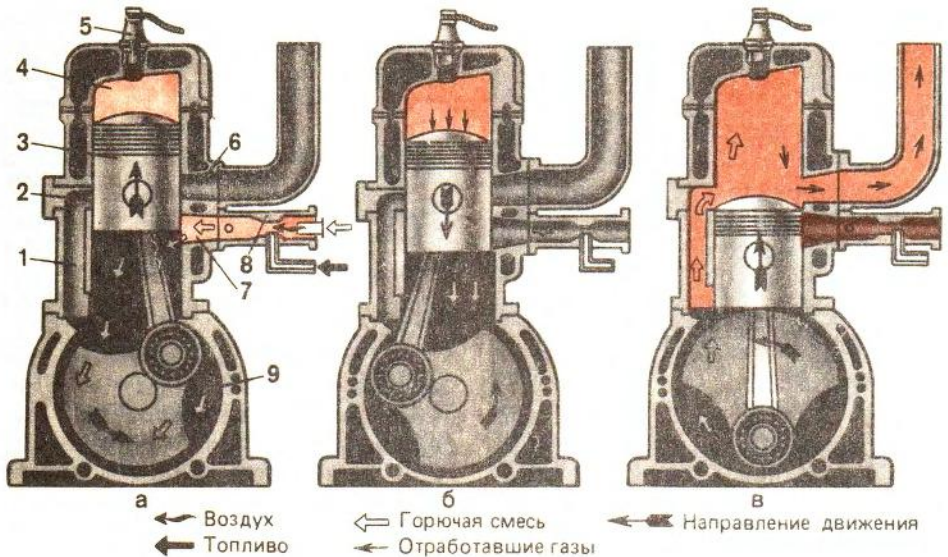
Схемы устройства и работы двухтактного карбюраторного двигателя:
